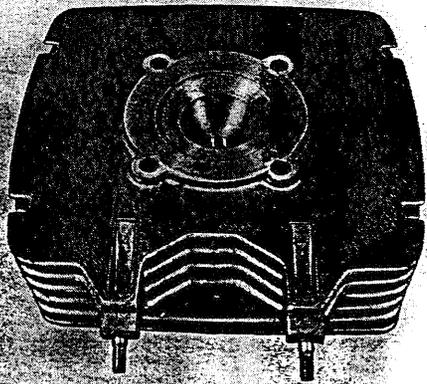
Surface d'étanchage du couvercle de cylindre et chambre de combustion
